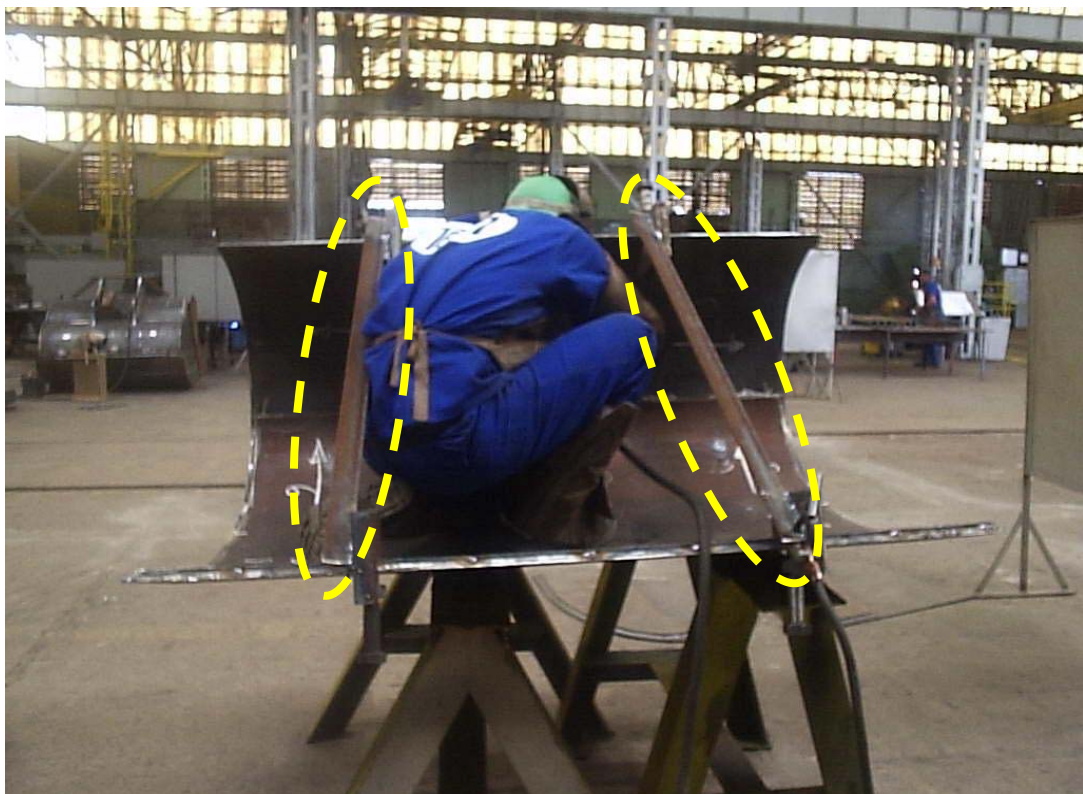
Dispositivo para montagem e soldagem do SC01.
